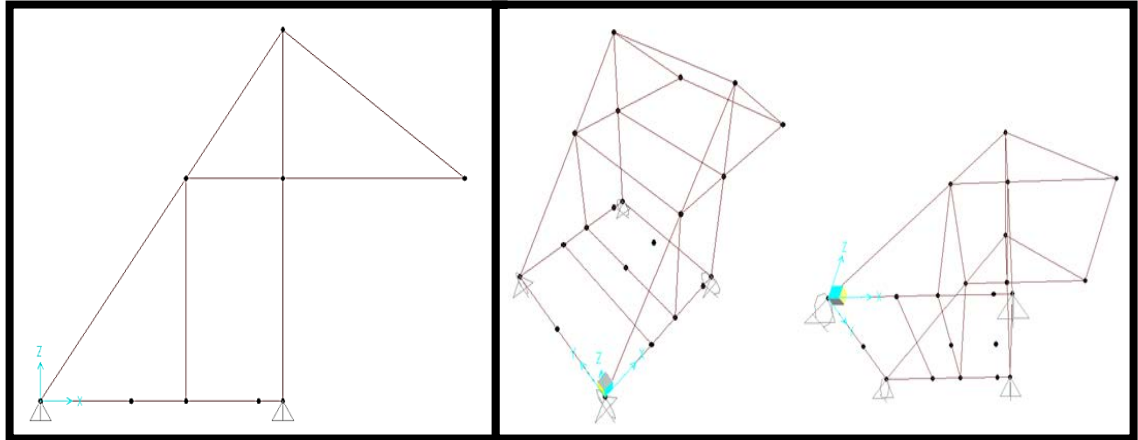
Grilla de la Grúa de Desplazamiento en terrazas para fachadas
